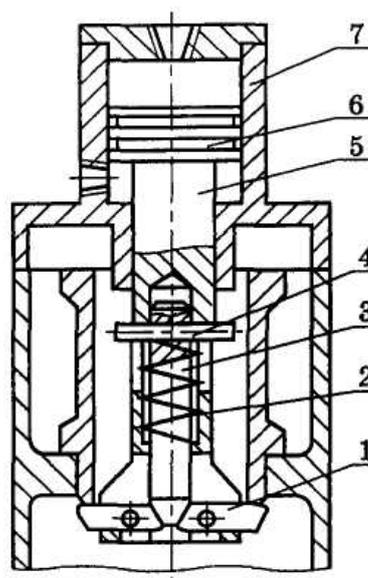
Устройство для снятия гильзы цилиндра: 1 – захват; 2 – пружина; 3 – клин; 4 – штифт; 5 – шток; 6 – поршень; 7 – гидроцилиндр
